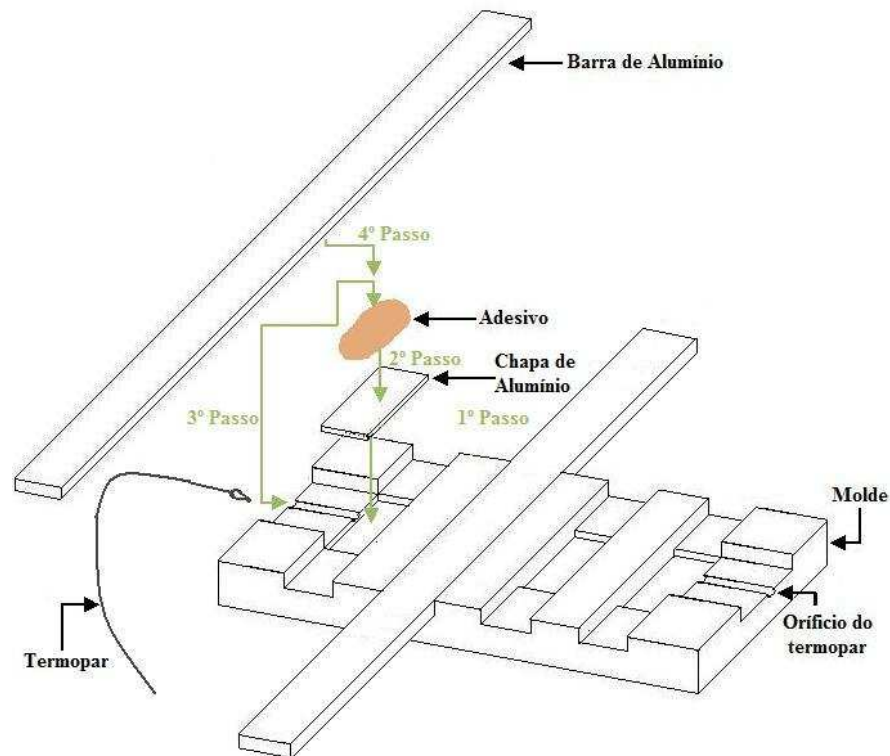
Esquema de montagem do molde no fabrico de provetes de referência.
